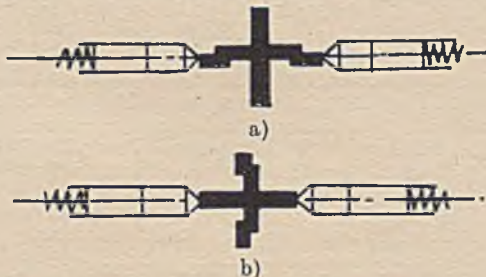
Kreuzschlüssel für Zentralschloßanlagen
